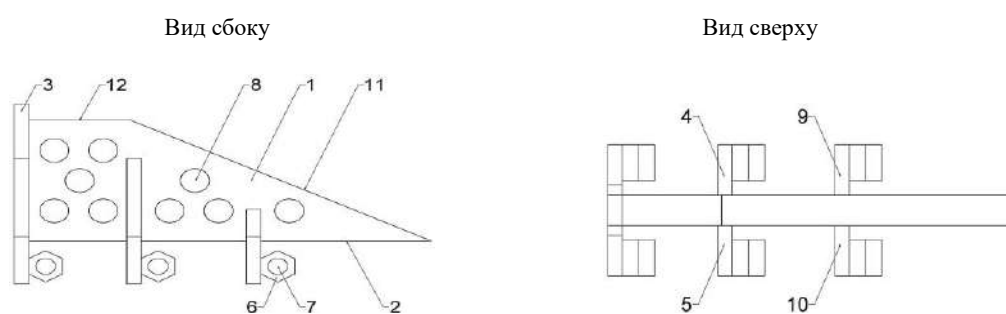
Устройство для поднятия колесной пары тепловоза:
